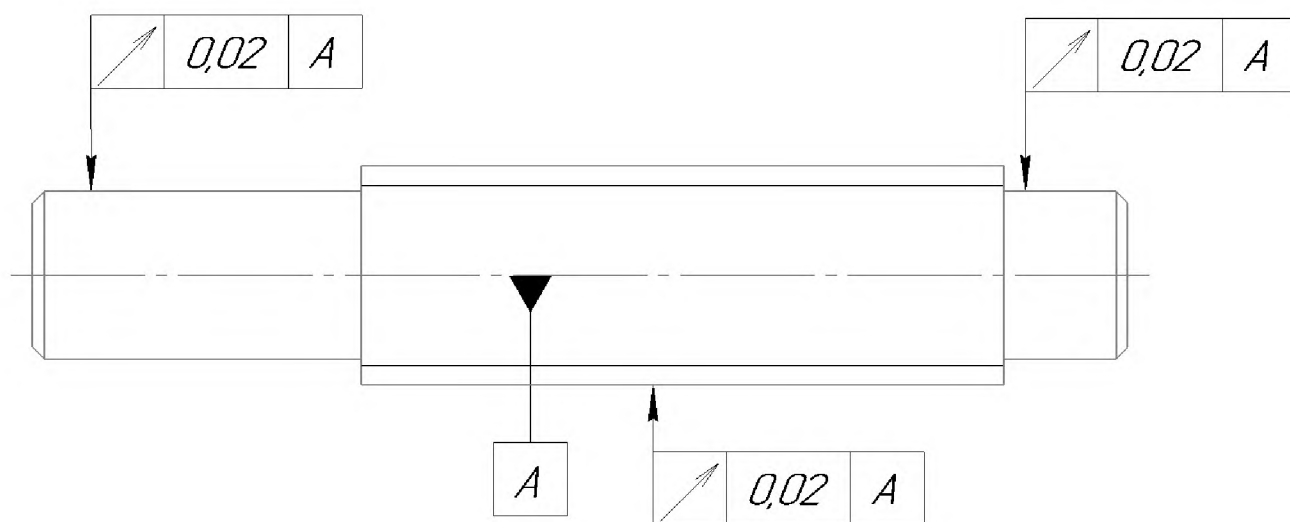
Відхилення форми та розташування поверхонь деталі
